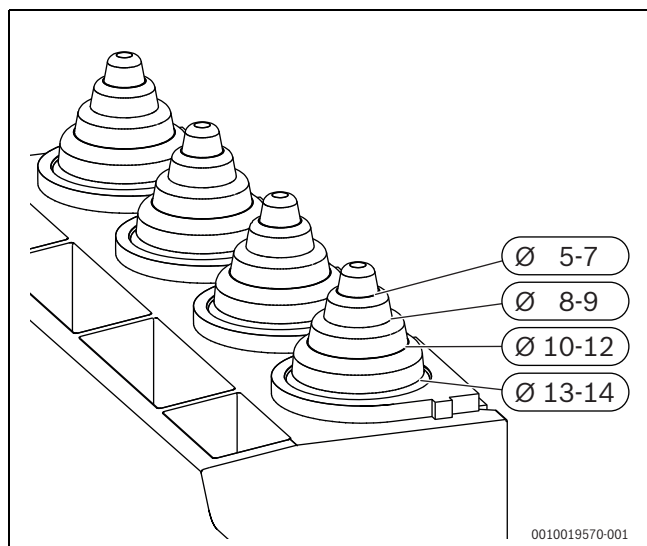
Zugentlastung an Kabeldurchmesser anpassen
